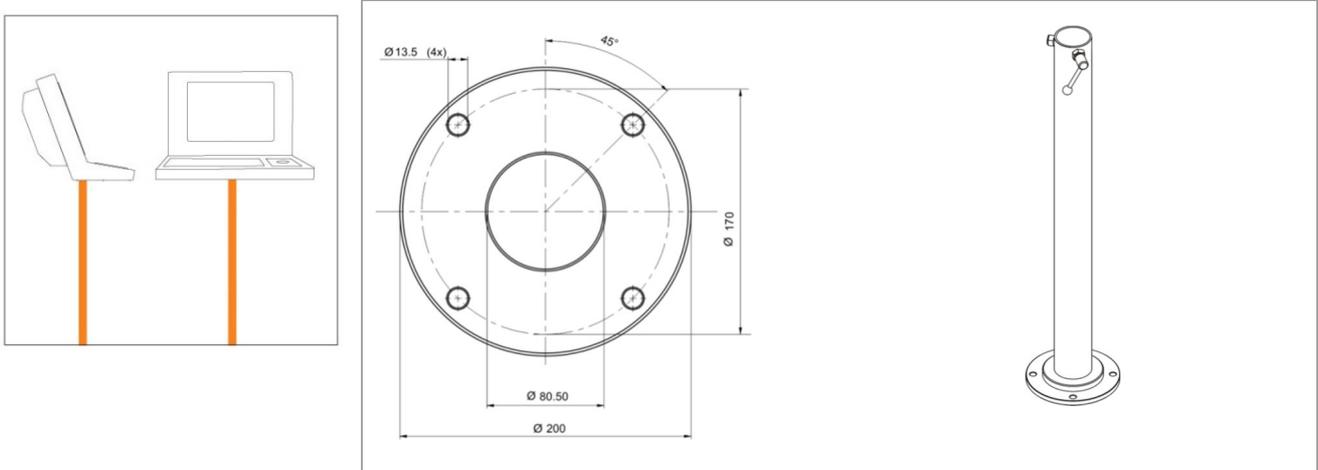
Bohrbild - Tragsystem für Bodenmontage
